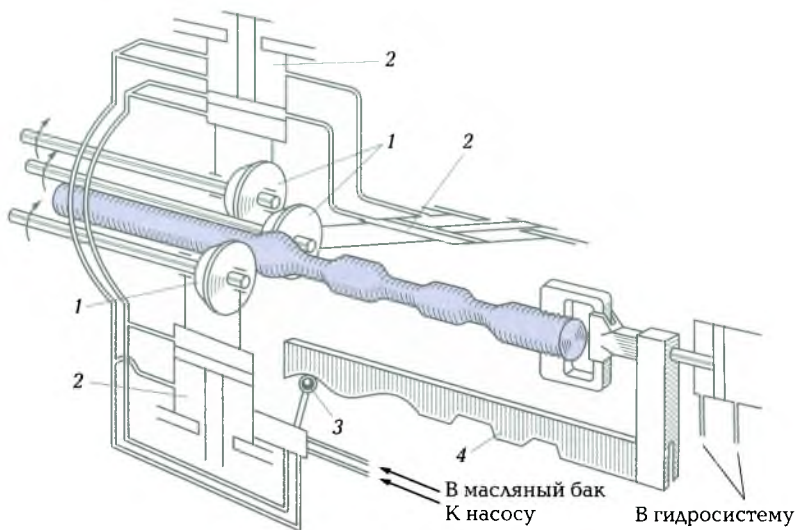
Схема получения заготовки переменного профиля на трехвалковом стане:
